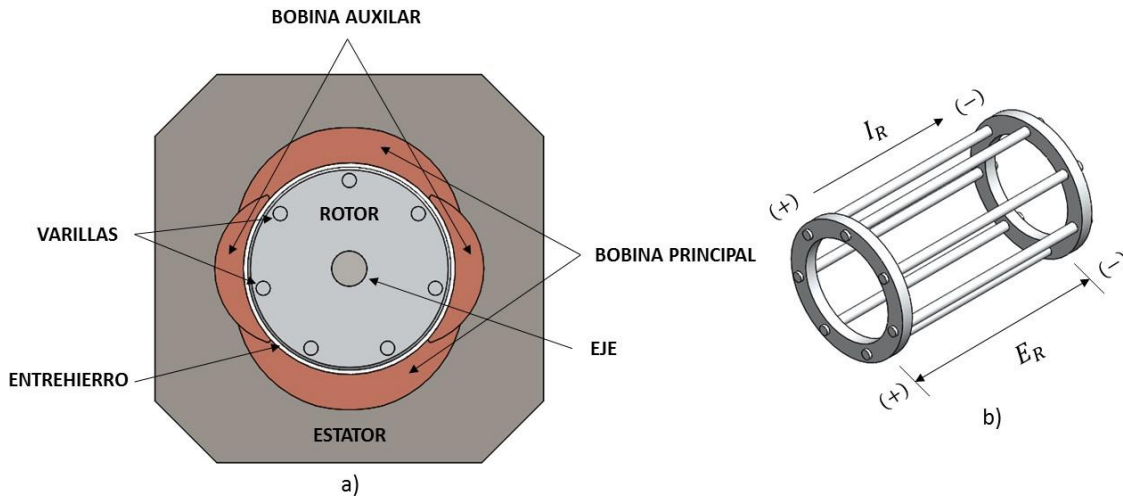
Motor monofásico: a) partes del motor, b) rotor jaula de ardilla, (fuente: el autor).
